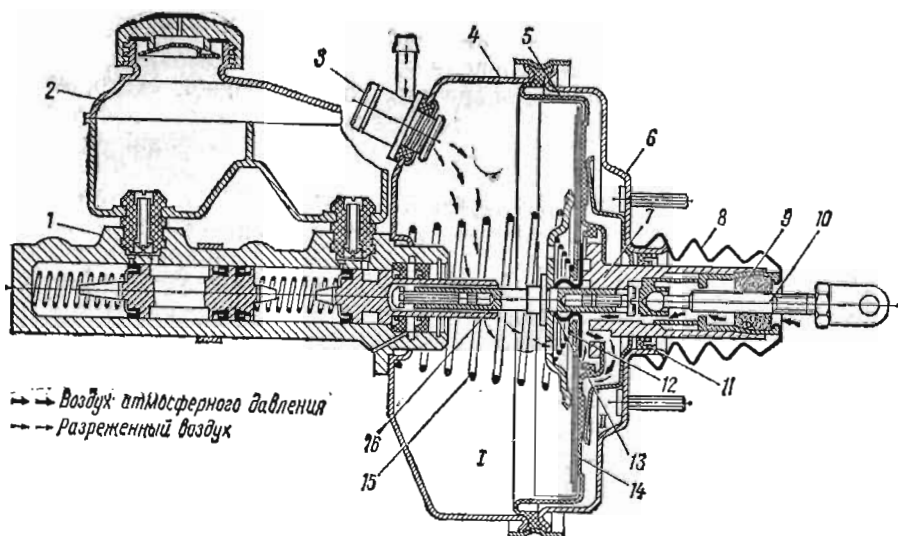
Вакуумный усилитель с главным тормозным цилиндром автомобиля «Москвич-2140»:
